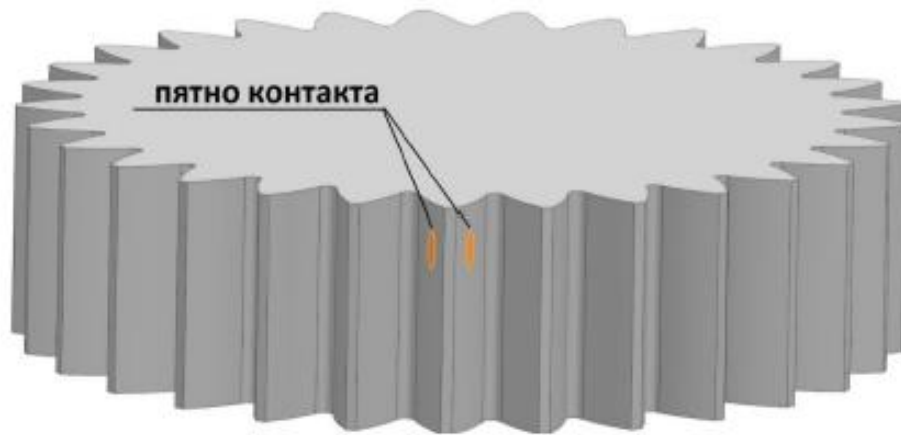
Форма плями контакту зубчастого колеса із черв'ячним
